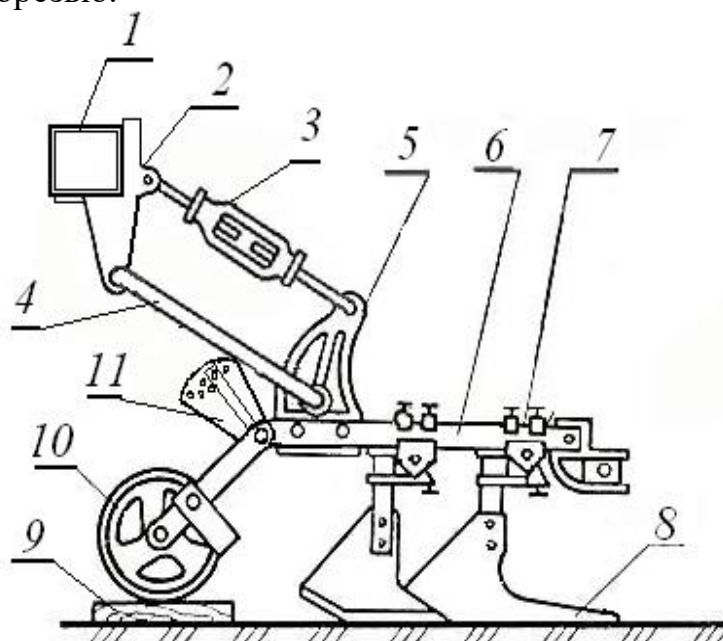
Культиватор УСМК-5,4: 1 – рама; 2 – передний кронштейн; 3 – регулируемое звено; 4 – нижнее звено; 5 – задний кронштейн; 6 – грядиль; 7 – узел крепления рабочих органов; 8 – лапа; 9 – деревянный брус; 10 – опорное колесо секции; 11 – механизм регулировки глубины обработки
